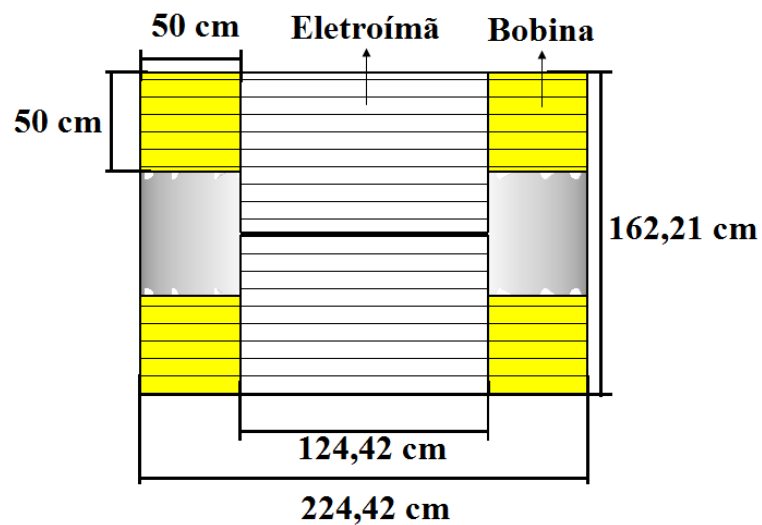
Dimensões e posicionamento das bobinas principais e eletroímã principal
